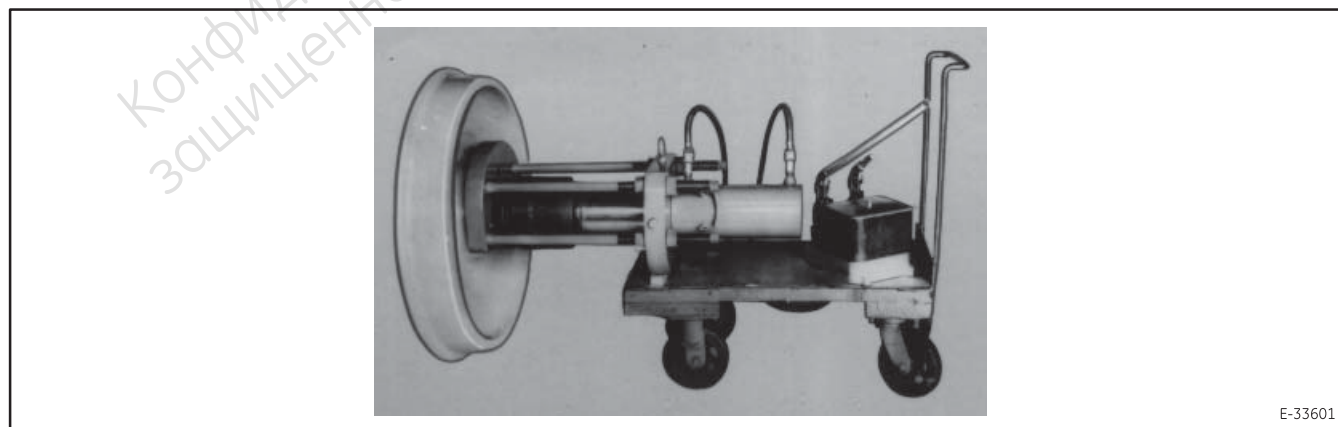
Распрессовка буксового подшипника с помощью передвижной установки.
